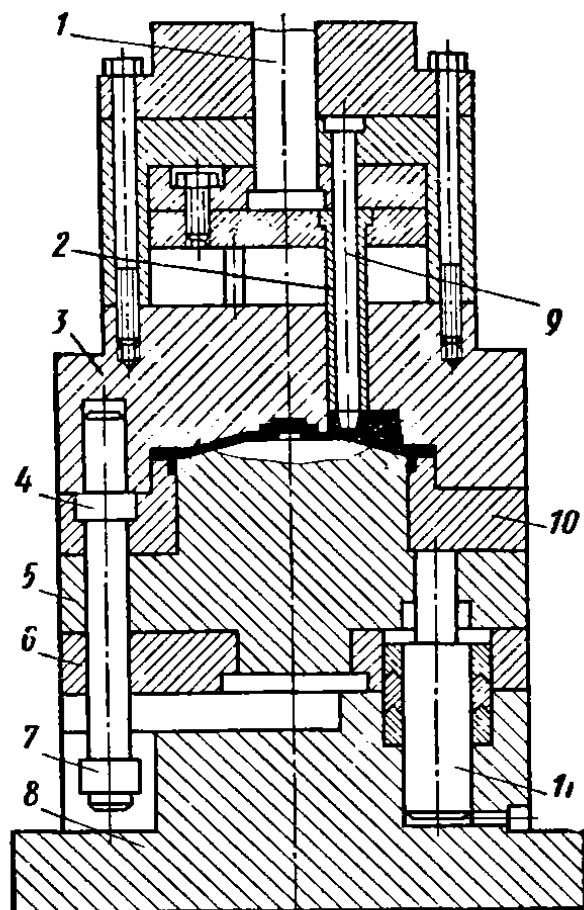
Приспособление для штамповки из жидкого металла:
